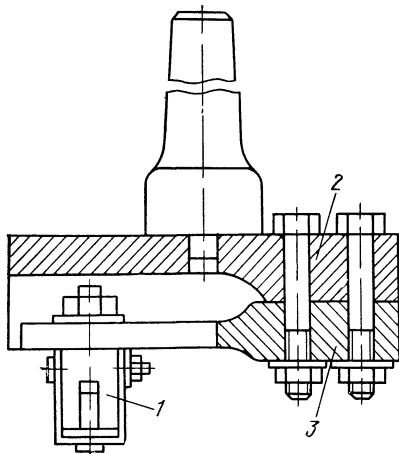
Устройство с пластинчатой пружиной для обкатки плоских поверхностей
